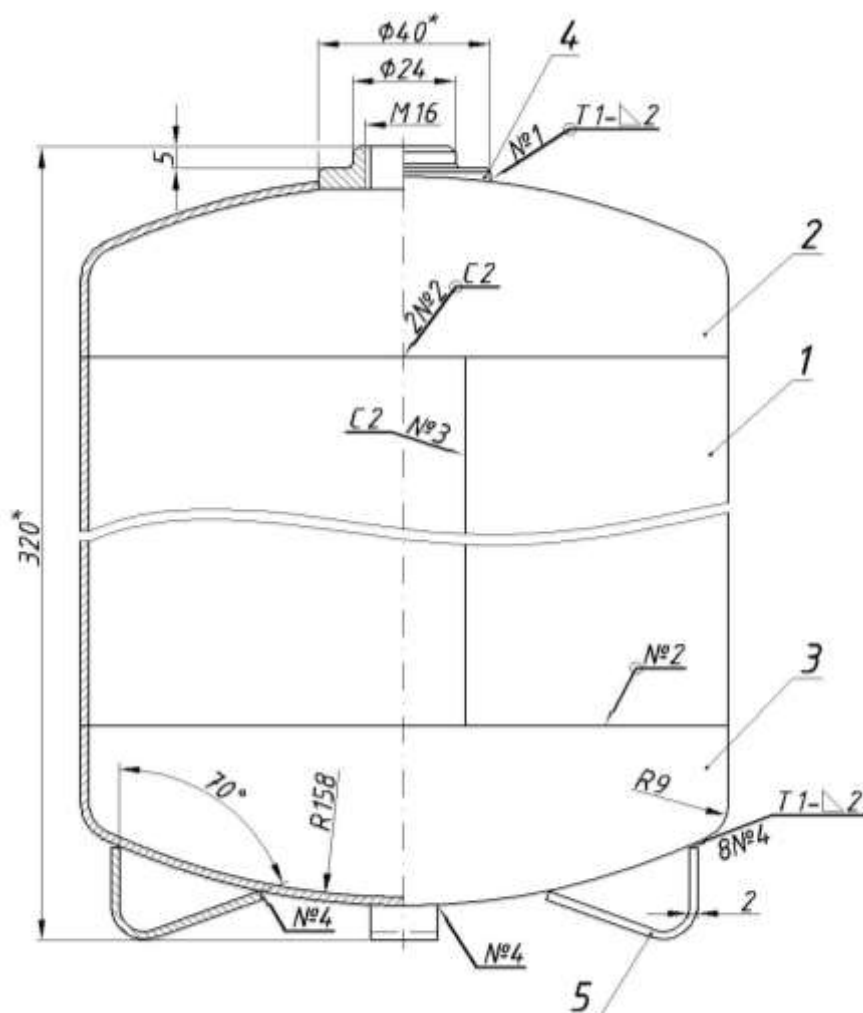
Загальний вигляд корпусу вогнегасника ВП-3
